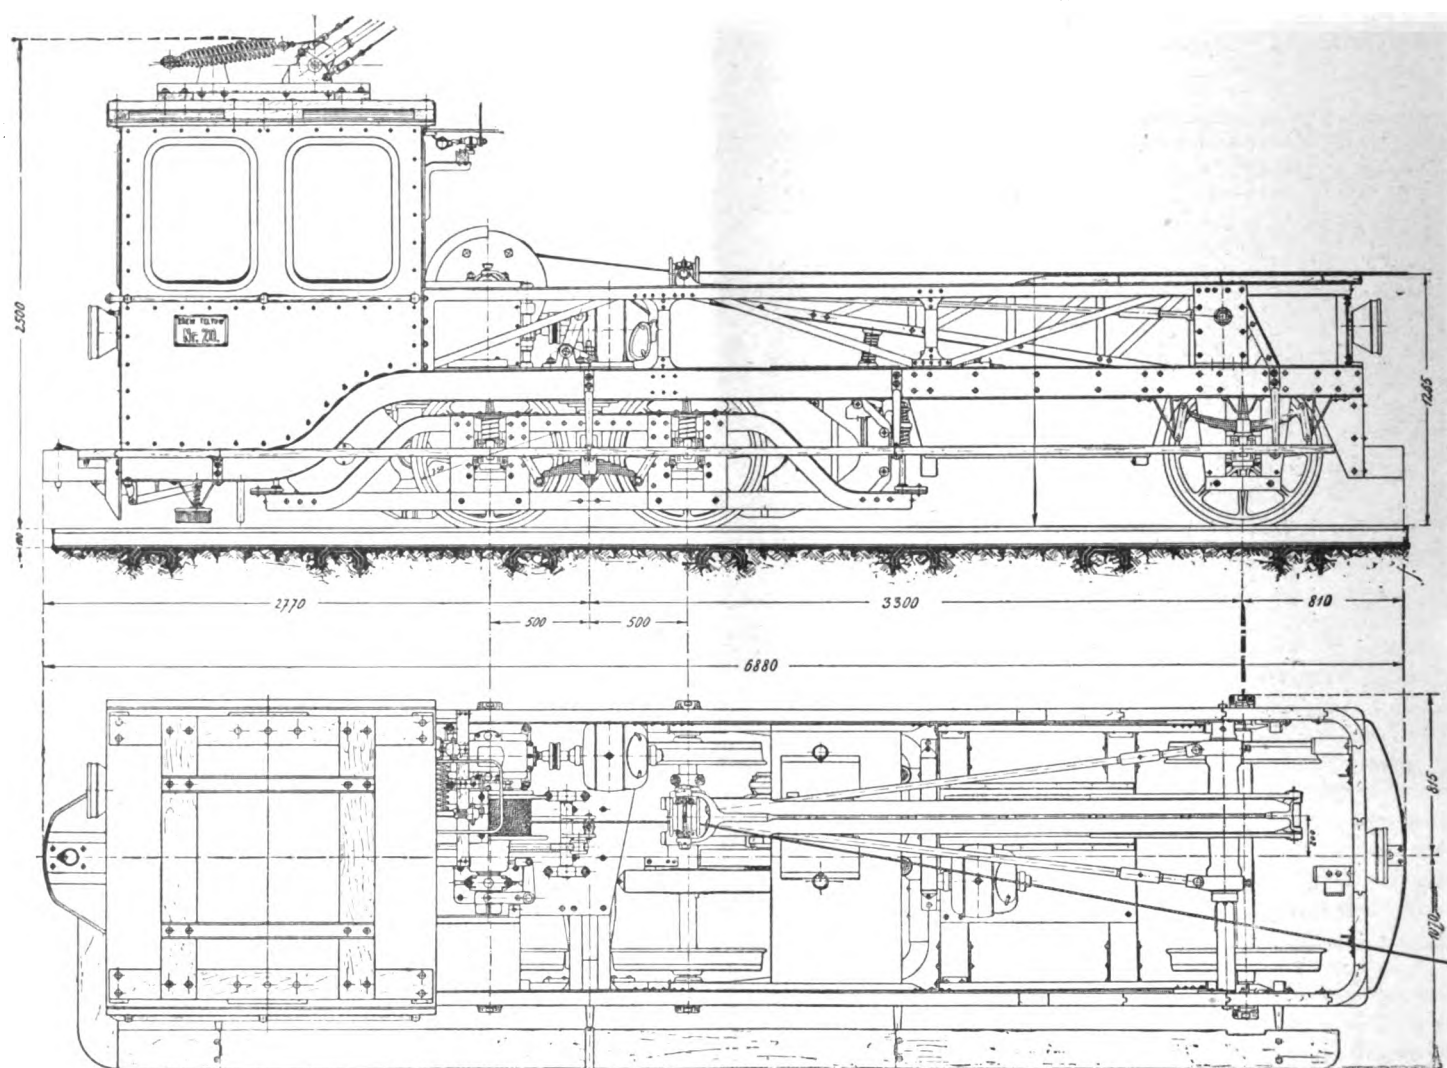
e 16 — Locomotore elettrico per il rimorchio di galleggianti. - Elevazione e pianta.
